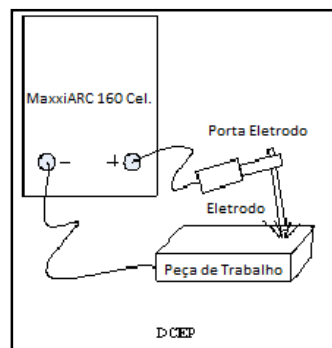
Conexão positiva para soldagem com eletrodo revestido
